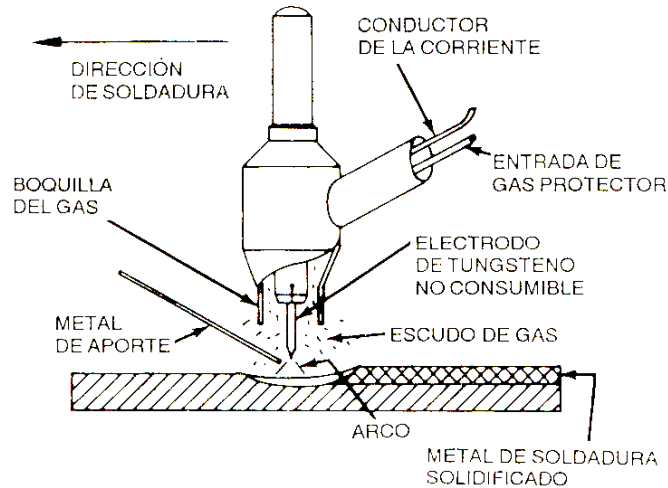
Esquema del proceso de soldadura por arco de tungsteno
